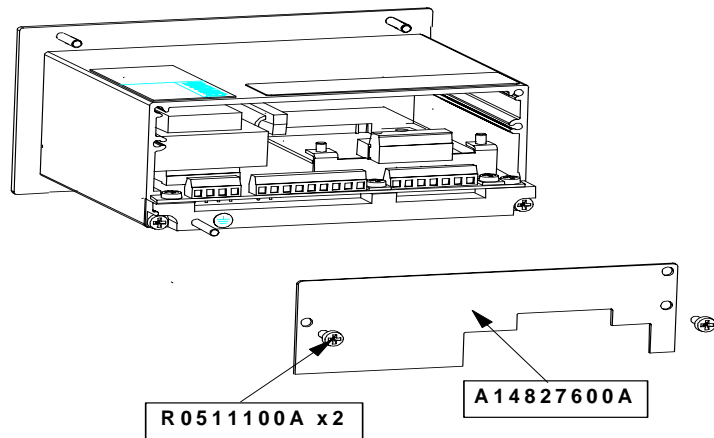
Instalación de la PCB Allen-Bradley en el gabinete de montaje en panel
